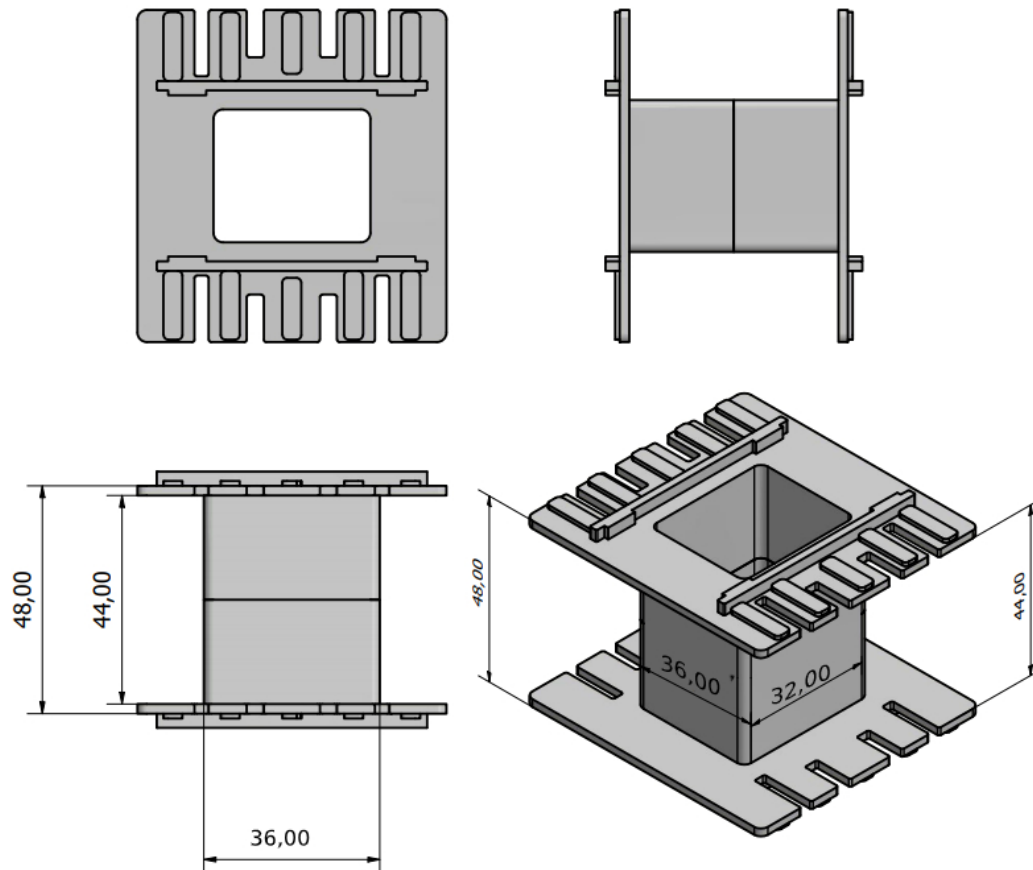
Dimensiones del carrete (Dimensiones en [mm]).
